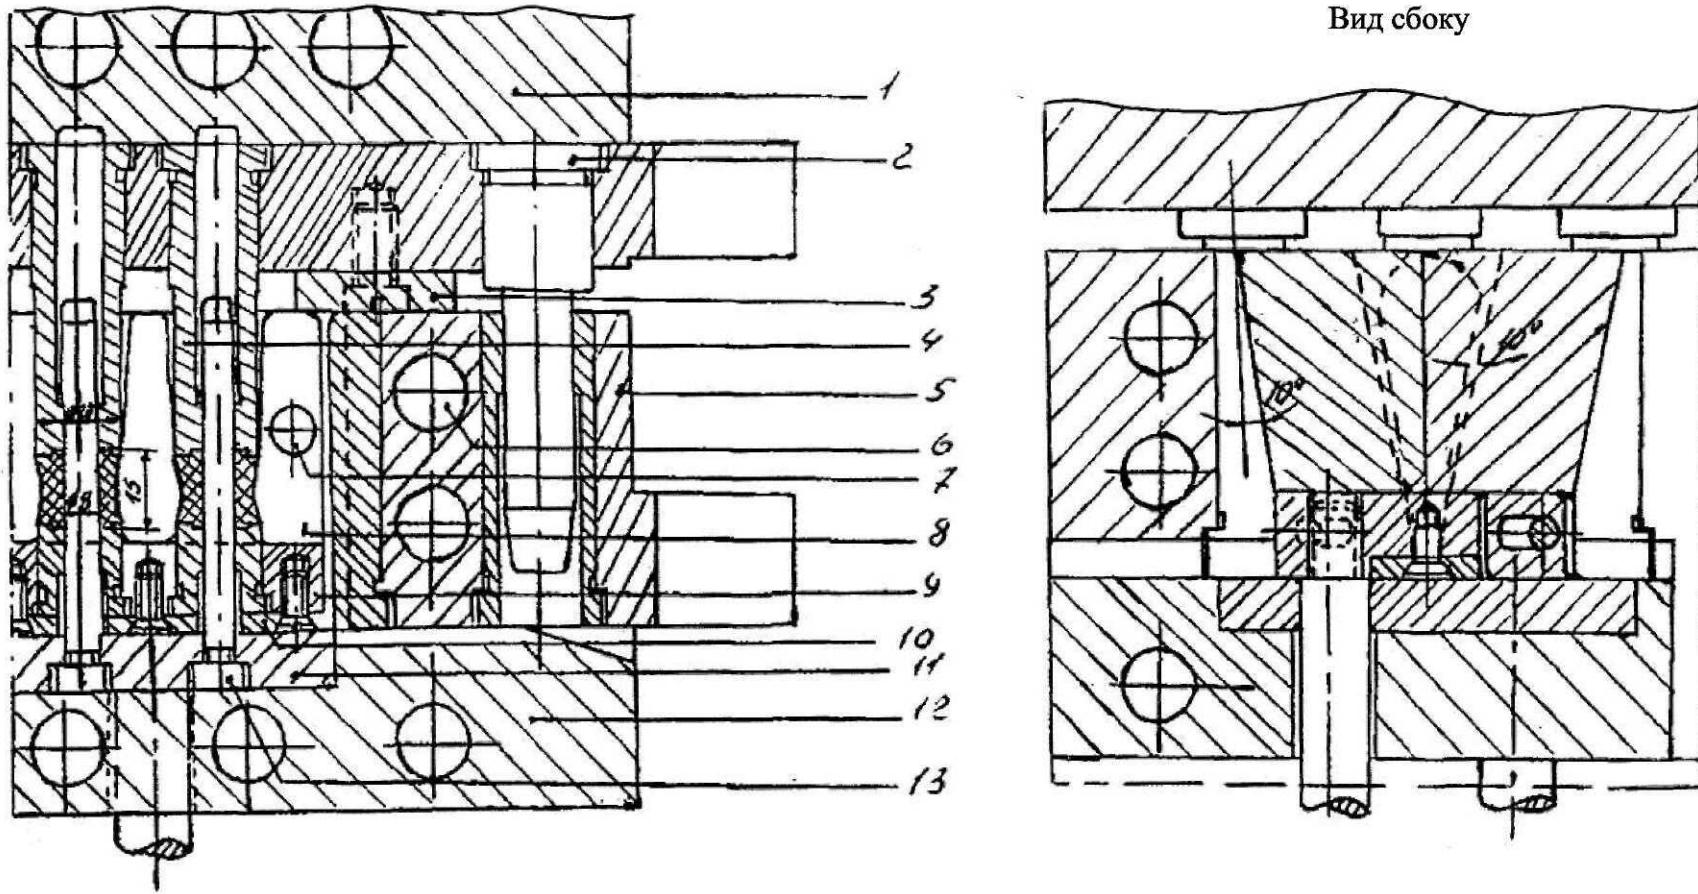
Пресс-форма для изготовления деталей методом прессования:
